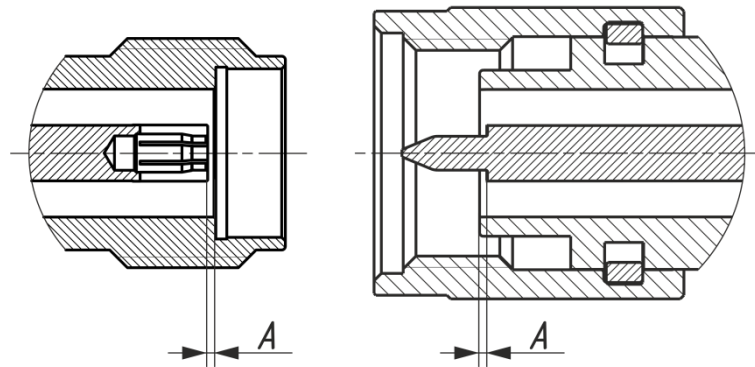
Соединители тип 3,5 мм и IX (розетка и вилка)
